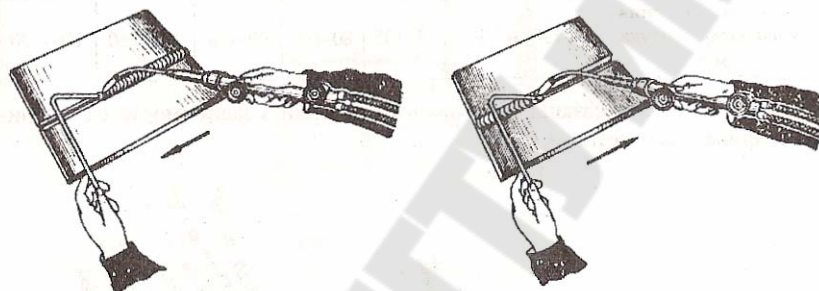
Способы выполнения газовой сварки: а - левый, б - правый
